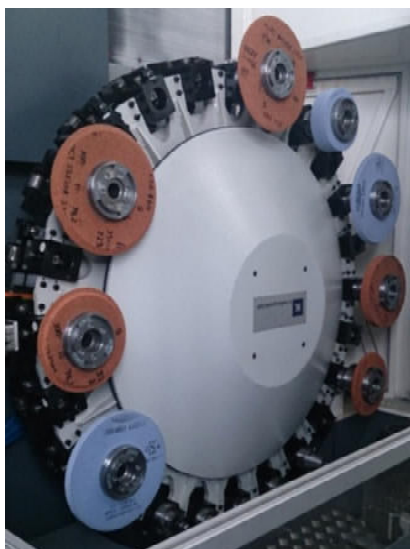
Инструментальный магазин шлифовального станка вмещает 12 позиций шлифовальных кругов диаметром 300 мм или 24 позиции для осевого инструмента
